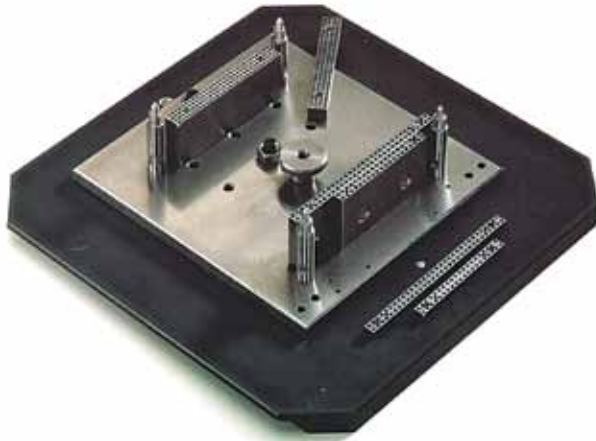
Матрица для запрессовки РС/104 и РС/104+
